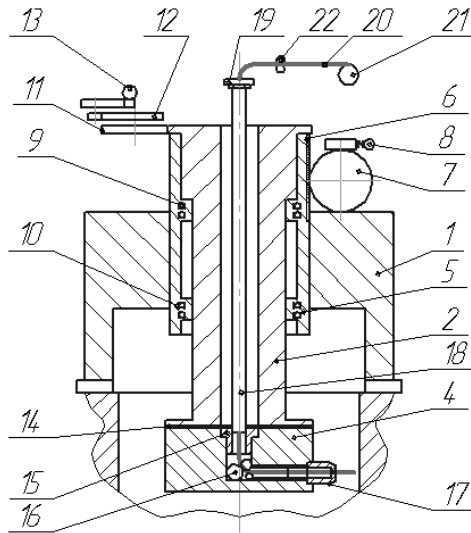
Схема наплавлення поверхнь отворів неповоротних деталей
